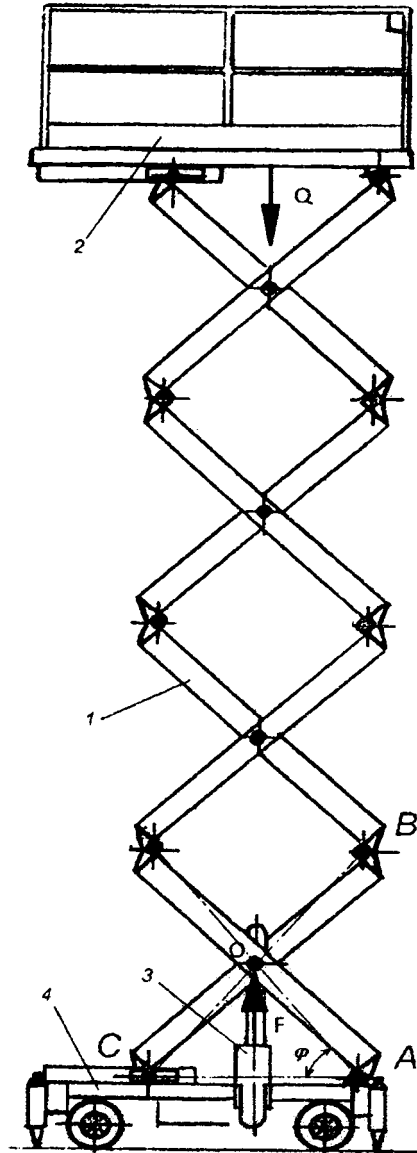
Схема ножничного механизма с центральным вертикальным расположением привода
